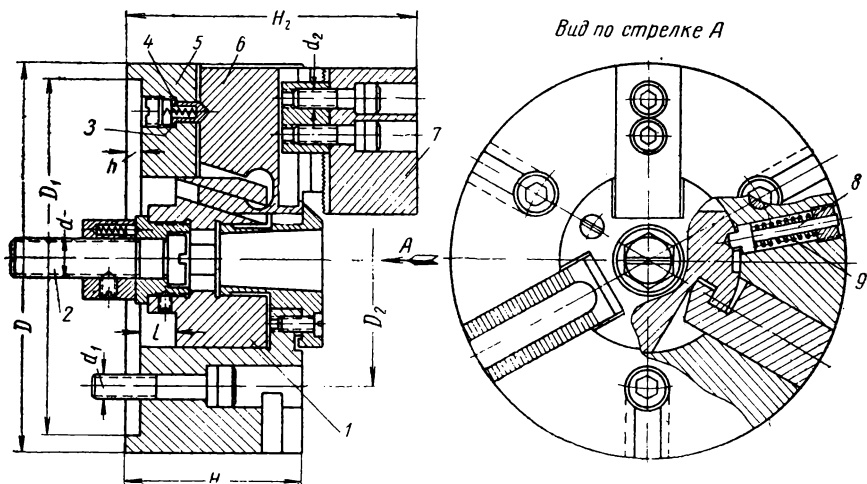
Трехкулачковый клино-рычажный патрон.
